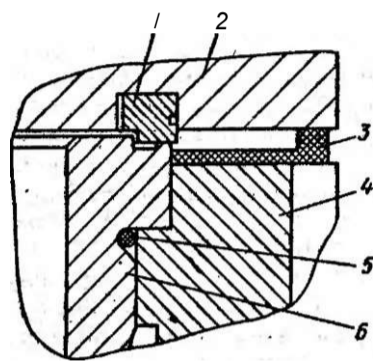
Стыки головки цилиндра и гильзы, головки и блока цилиндров:
